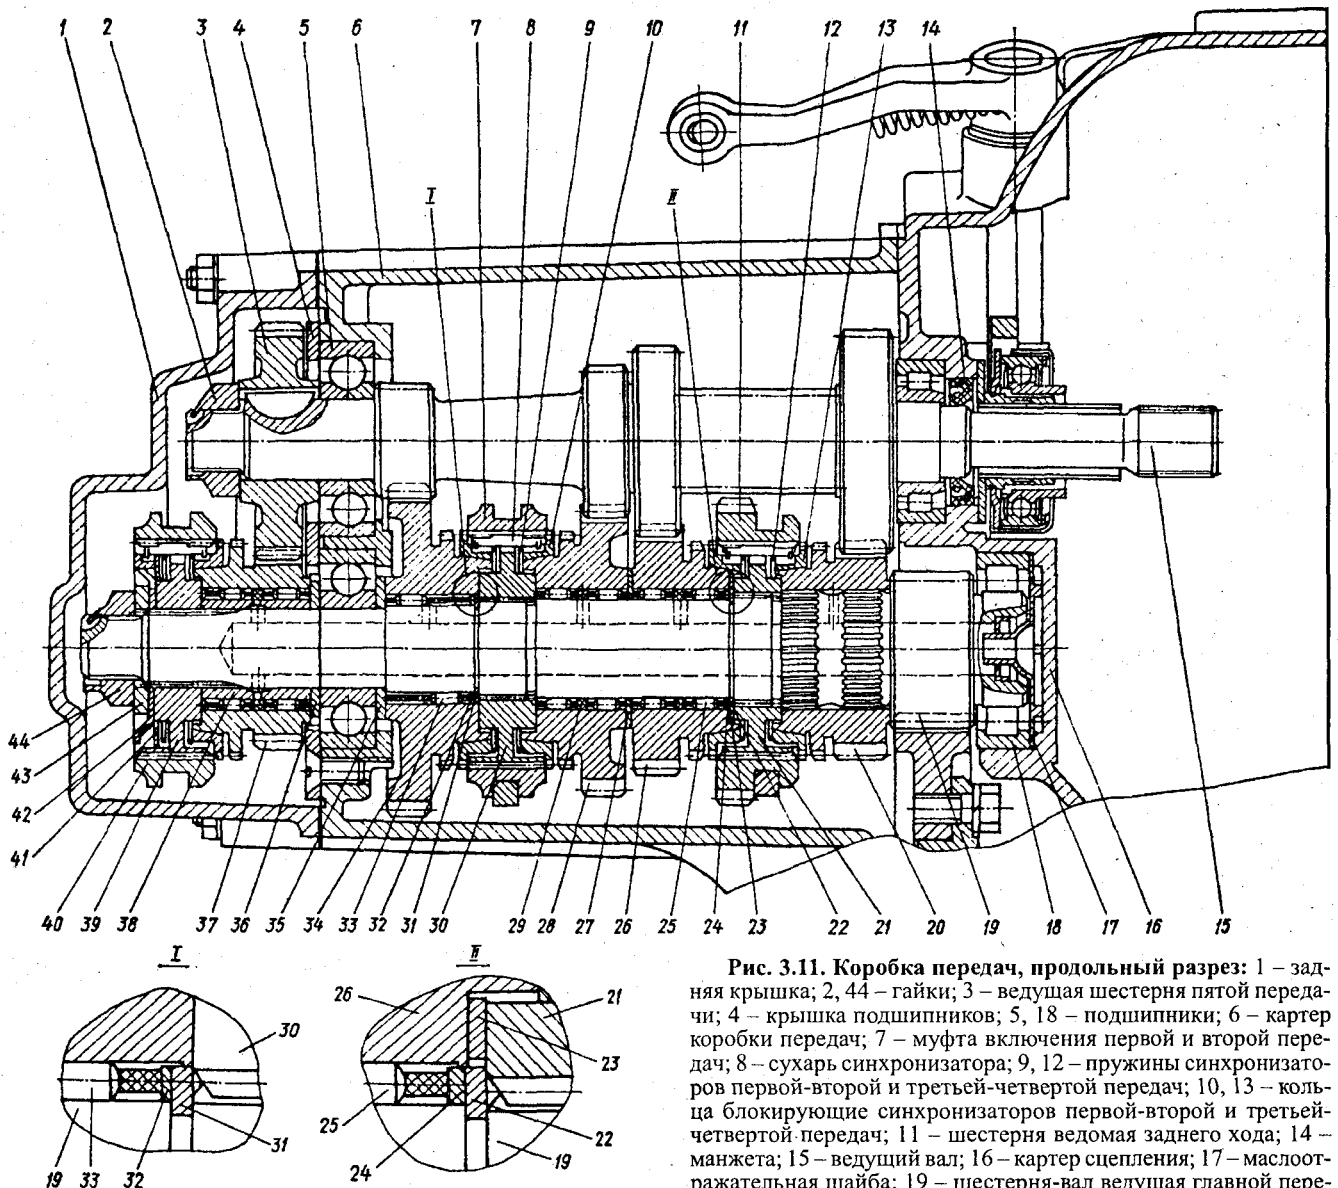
Коробка передач, продольный разрез: 1 – задняя крышка; 2, 44 – гайки; 3 – ведущая шестерня пятой передачи; 4 – крышка подшипников; 5, 18 – подшипники; 6 – картер коробки передач; 7 – муфта включения первой и второй передач; 8 – сухарь синхронизатора; 9, 12 – пружины синхронизаторов первой-второй и третьей-четвертой передач; 10, 13 – кольца блокирующие синхронизаторов первой-второй и третьей-четвертой передач; 11 – шестерня ведомая заднего хода; 14 – манжета; 15 – ведущий вал; 16 – картер сцепления; 17 – маслоотражательная шайба; 19 – шестерня-вал ведущая главной передачи; 20, 26, 28, 34, 37 – ведомые шестерни четвертой, третьей,
